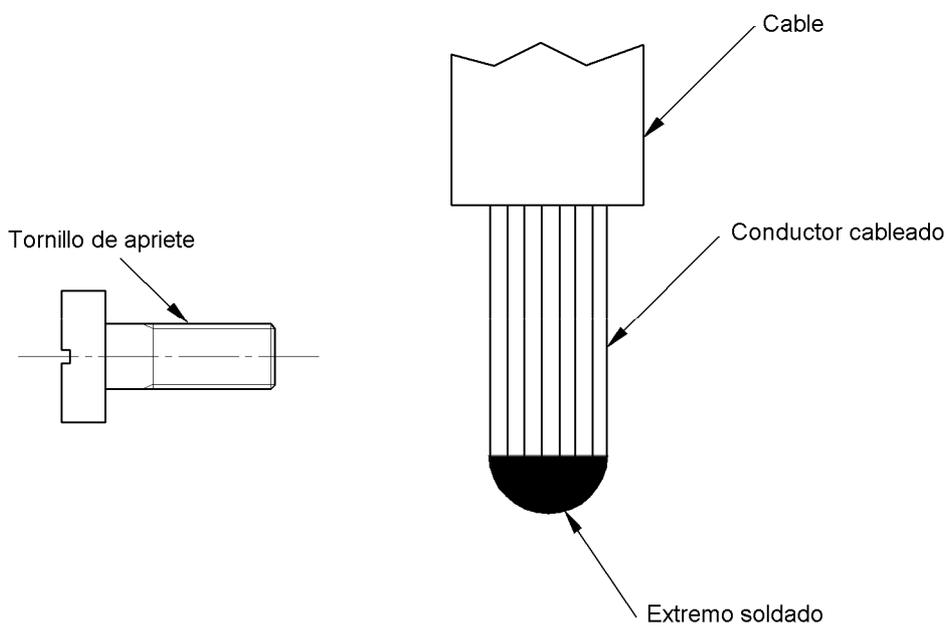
Ejemplo de grado permitido de soldadura
